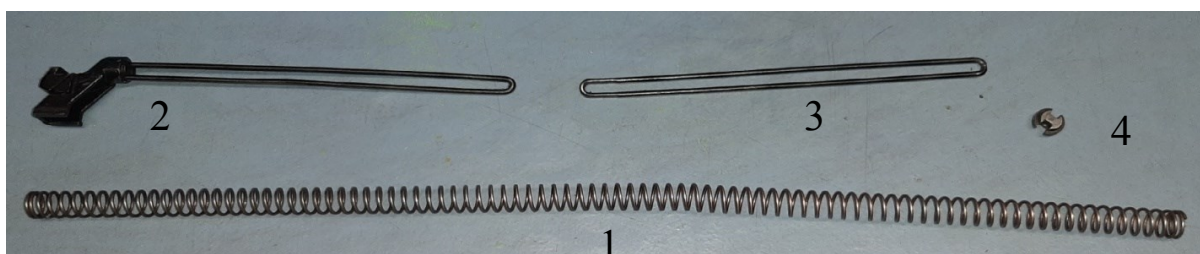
Возвратный механизм: 1 – возвратная пружина; 2 – направляющий стержень; 3 – подвижный стержень; 4 – муфта
